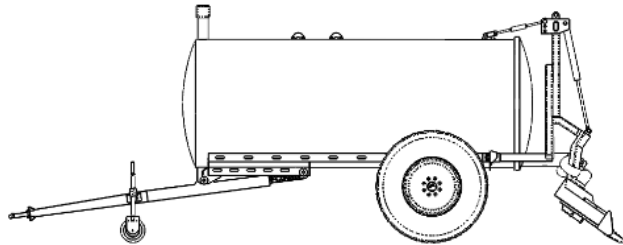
CAD – Zeichnungsansicht Anhänger
